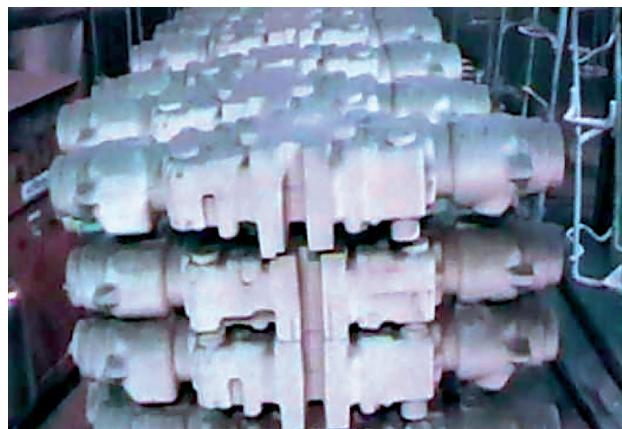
Пустотельные цилиндрокартерные стержни отливки «блок цилиндров» 240-1002015, изготовленные по Амин-процессу
